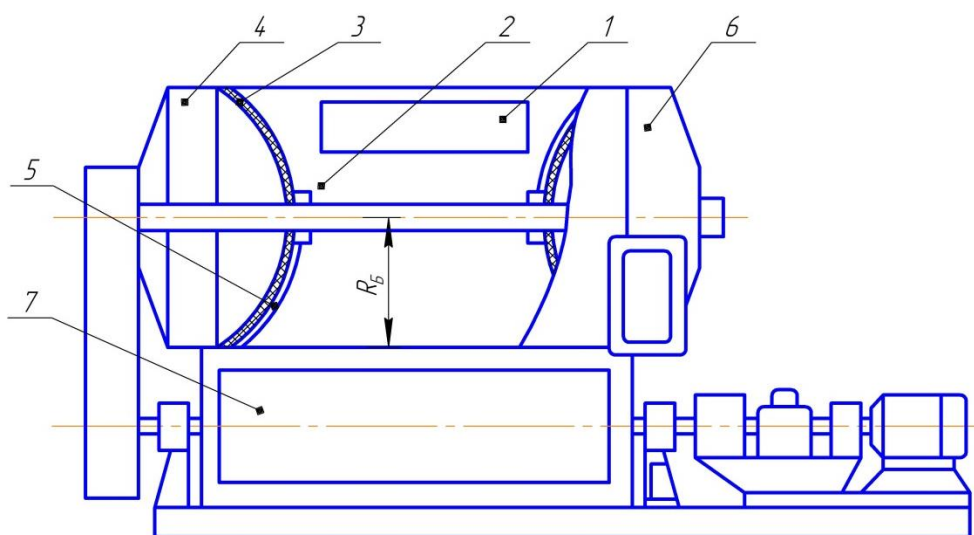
Схема сепаратора со сферической формой конструкции сетчатой поверхности камеры
